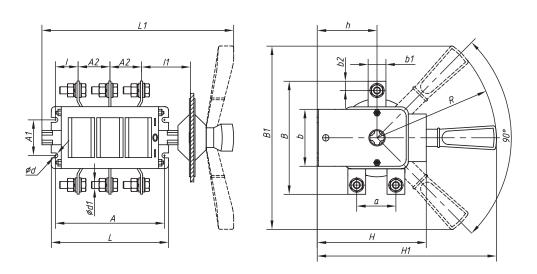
Выключатель-разъединитель универсальный трехполюсный на два направления с д/г камерами, съемная левая/правая рукоятка
